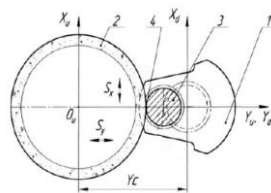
Схема розташування орієнтованого абразивного круга під час шліфування шатунних шийок: 1 - колінчастий вал, 2 - шліфувальний круг, 3 - шатунна шийка колінчастого вала, 4 - поточна точка контакту шліфувального круга з деталлю.
